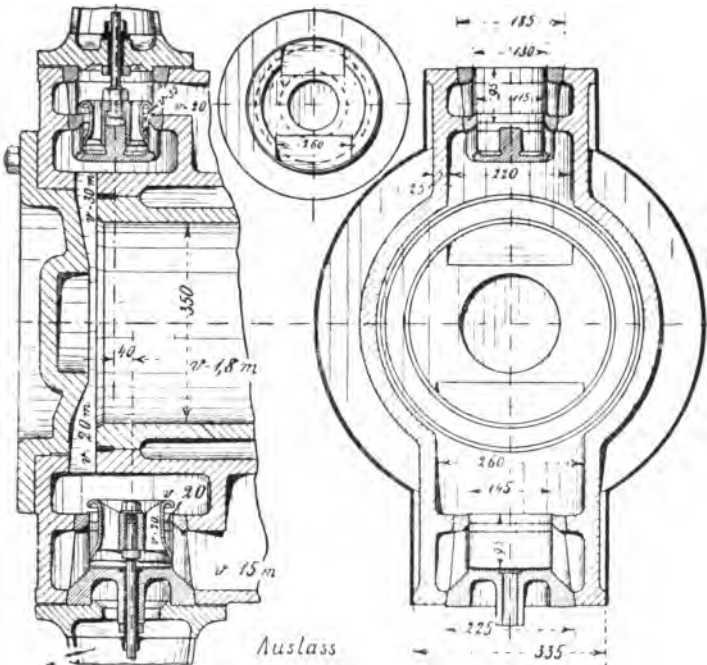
Ventilsteuerung für 350 mm Cylinderdurchmesser.
